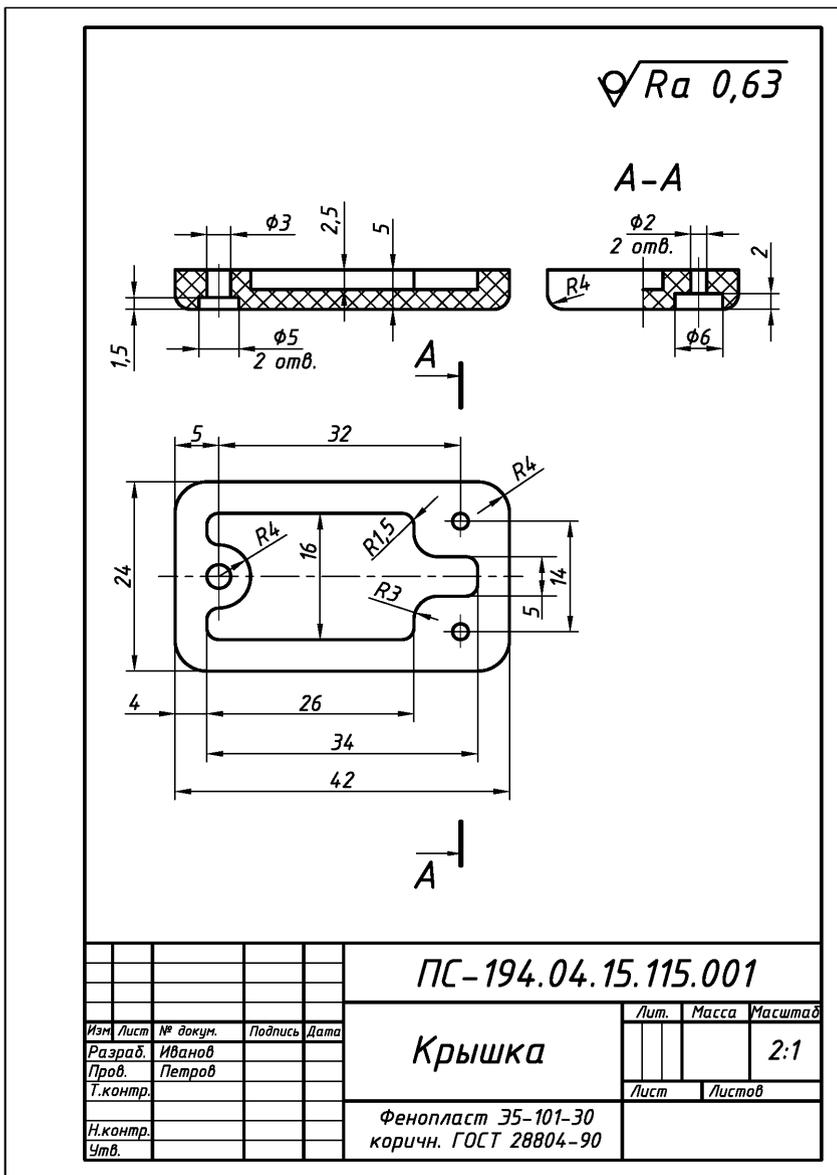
Оформление рабочего чертежа прессованной детали из пластмассы
